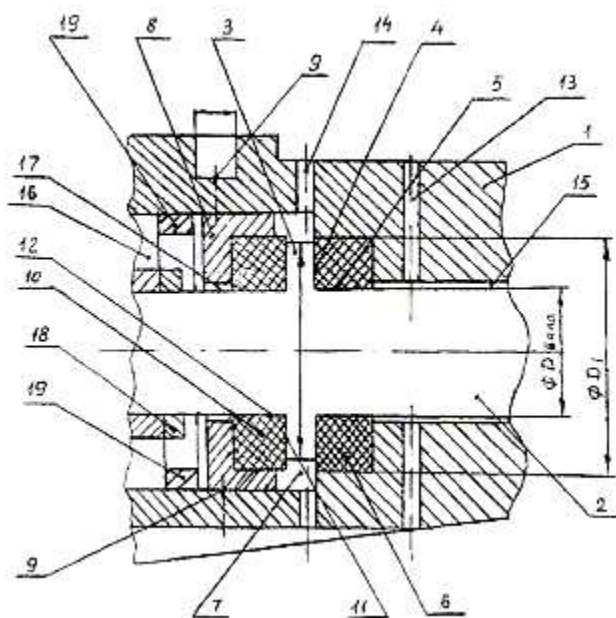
Подшипниковый узел со стороны приводного конца вала
